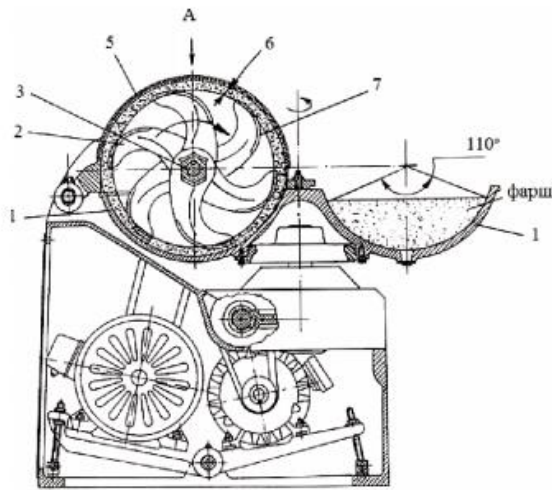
Схематичний розріз кутера, у якого ріжучі кромки ножів розгорнуті на кут  $\alpha$  щодо площини їх обертання: 1-чаша; 2-ріжучий ніж; 3-ножова головка; 4-площина обертання ножів; 5-кожух; 6-внутрішня бічна поверхня кругової зони обертання ножів; 7-ріжуча кромка ножа.
